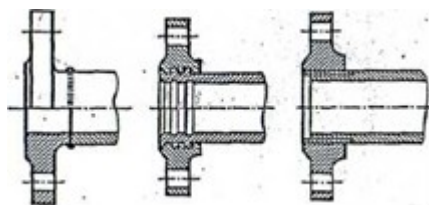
Соединения труб с фланцами: а — сваркой; б - развальцовкой; в — на резьбе
